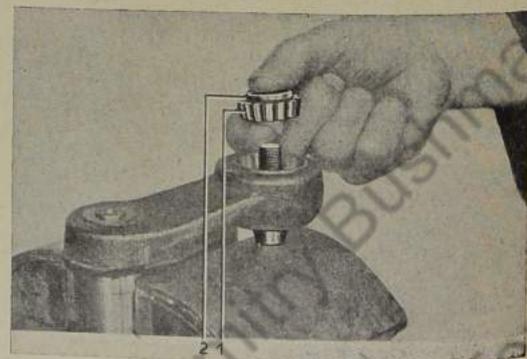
Inneren Laufring mit Kegelrollen einsetzen
